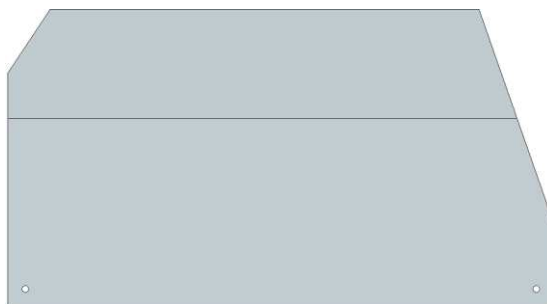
Schema dell'assemblaggio dei pannelli CFRP — Vista laterale
